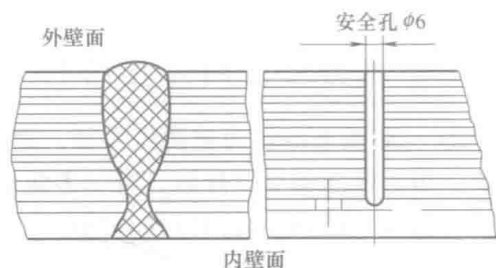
厚壁容器筒体及筒体环焊缝结构
